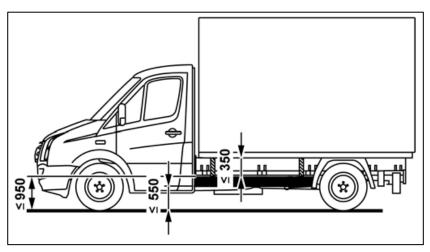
Positionnement du dispositif de protection latérale (schéma de principe)
